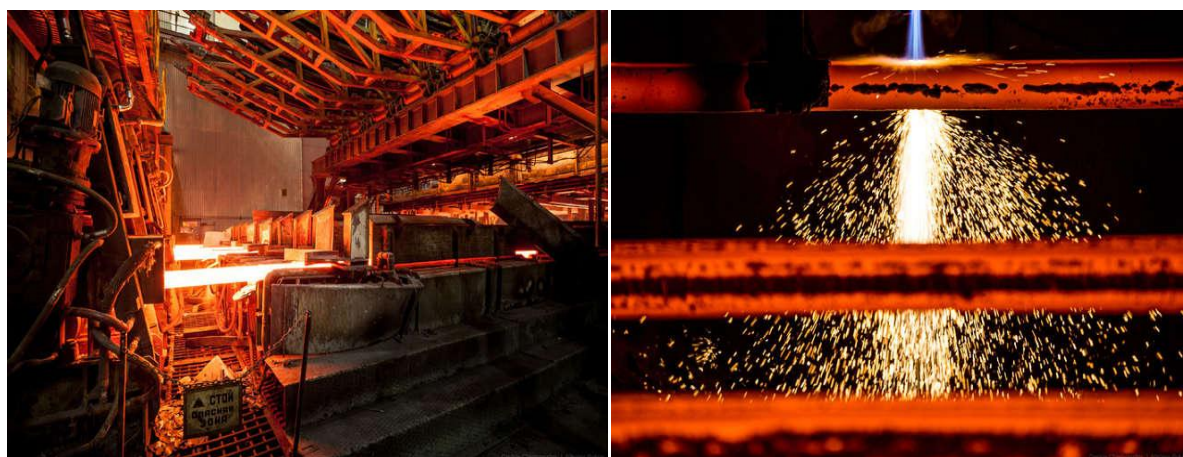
Порезка готовой рельсовой заготовки на МНЛЗ.
